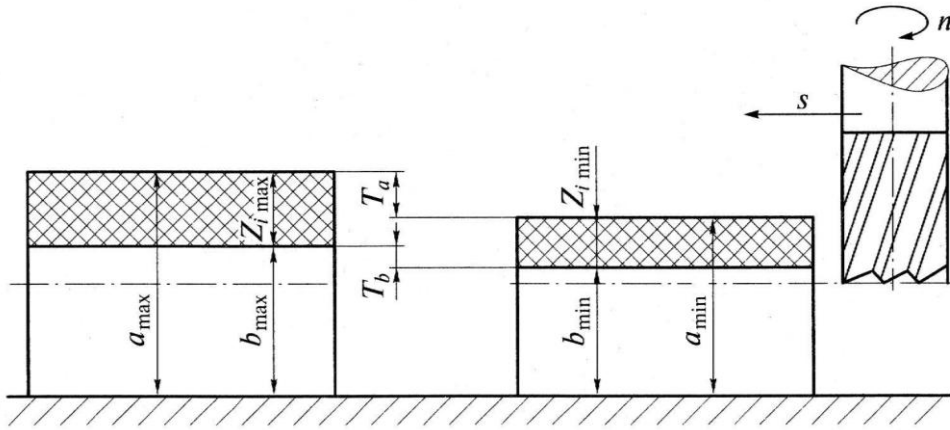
Схема для розрахунку проміжних розмірів заготовки
